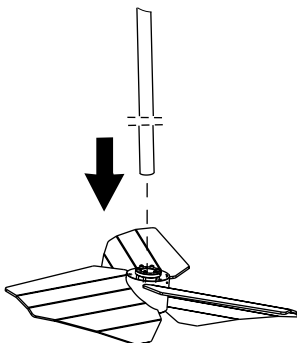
Трехлопастный сварной пропеллер с лопастями типа «гидроfoil»
